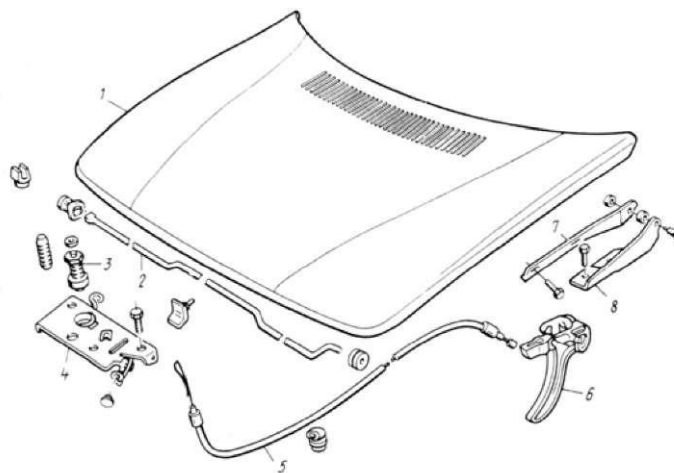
Капот двигателя автомобиля с механизмом открывания: 1 -капот; 2 -тяга; 3 - отпирающий палец; 4 -замок; 5 -трос капота; 6 - рукоятка открывания капота; 7 и 8 - шарниры
